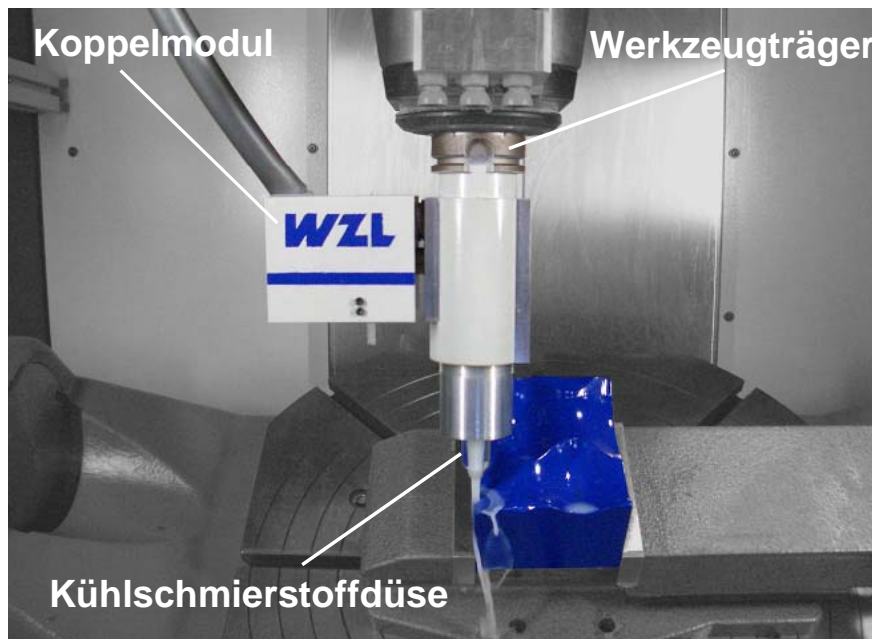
Maschinenintegrierter Ultraschallsensor im Einsatz
